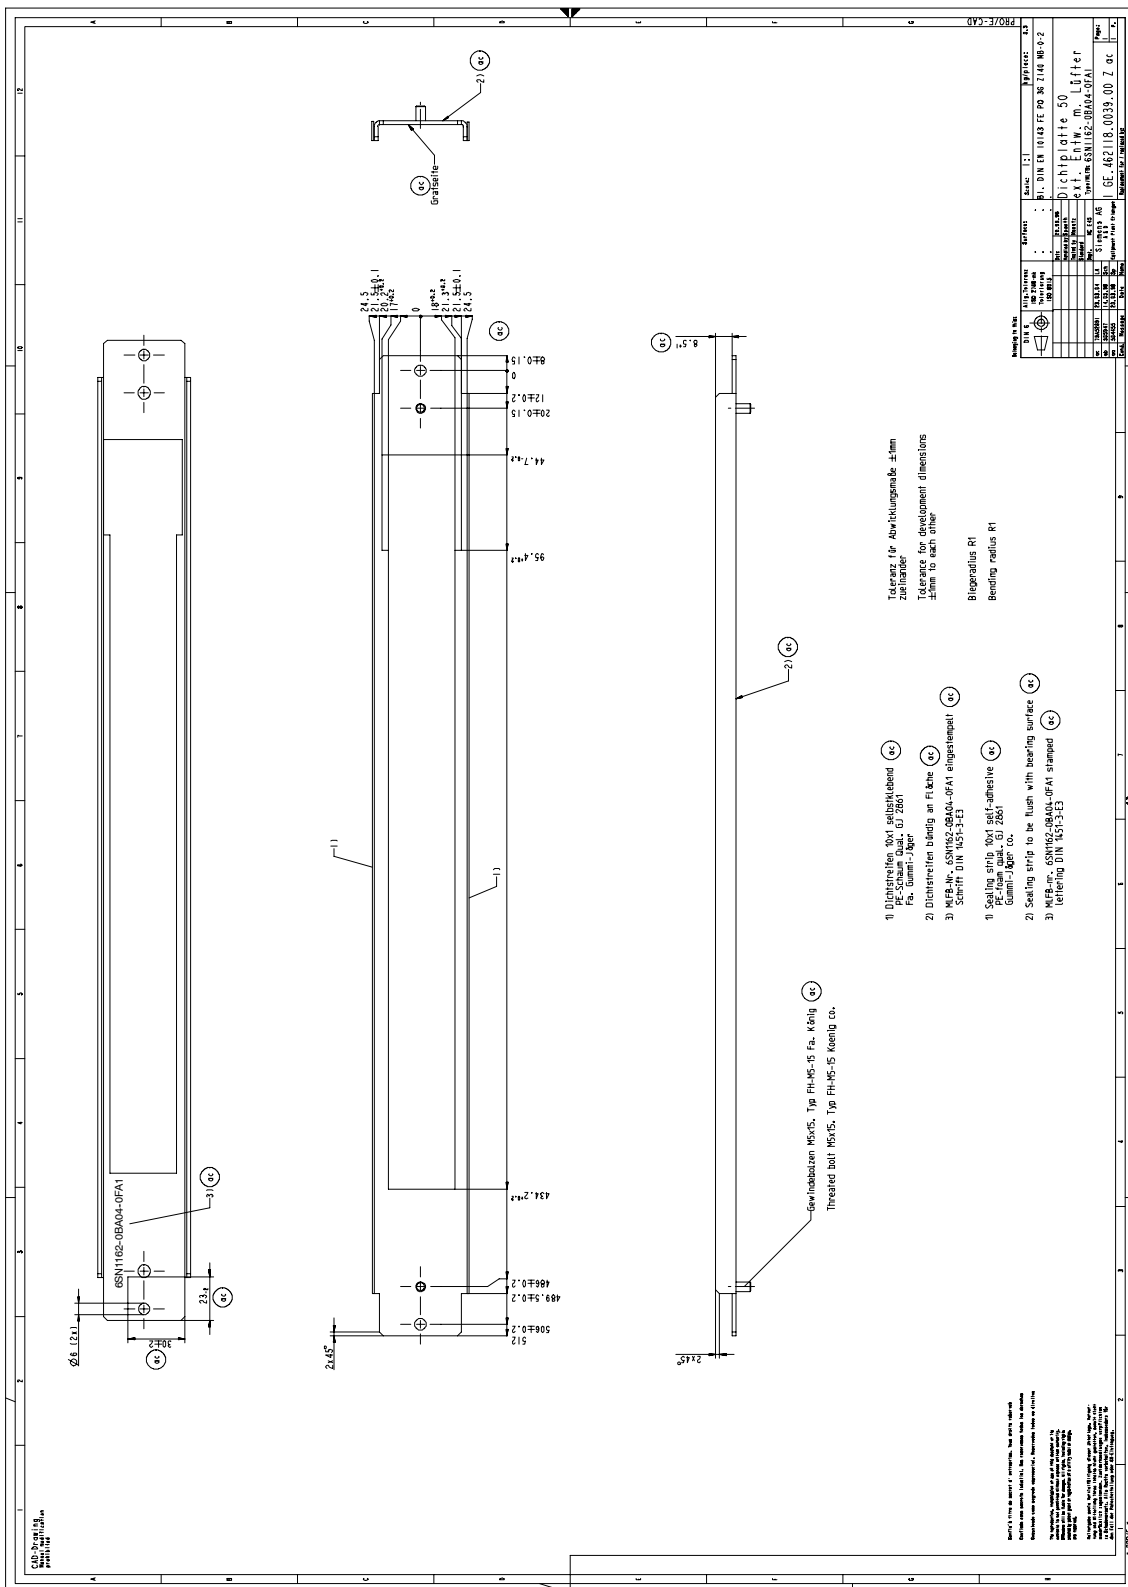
Refroidissement externe, châssis de montage pour le montage d'armoire Largeur de module 50 mm, 6SN1162-0BA04-0FA1
